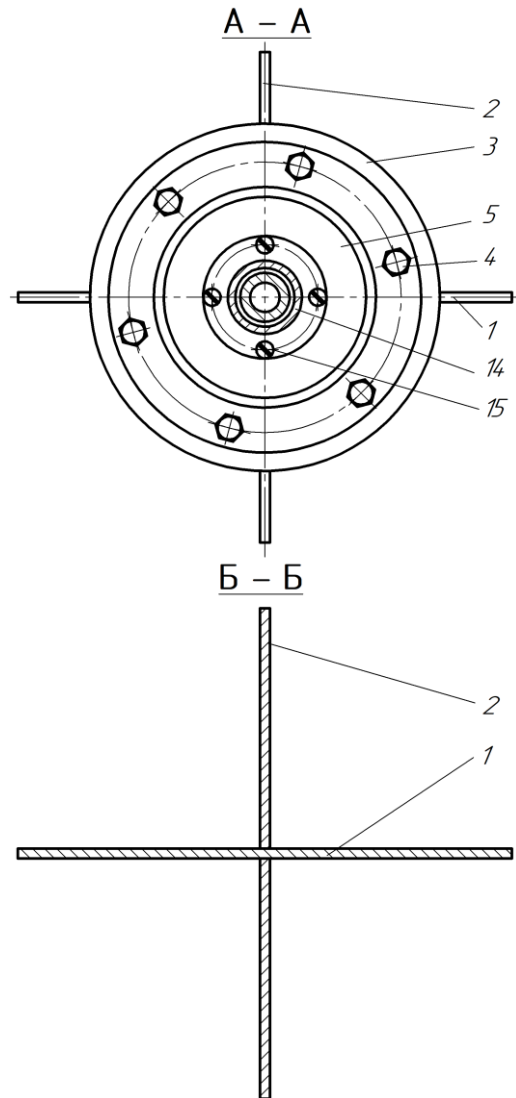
Общий вид крестообразного глубинного уплотнителя (Разрезы А – А и Б – Б на рис. 1)
